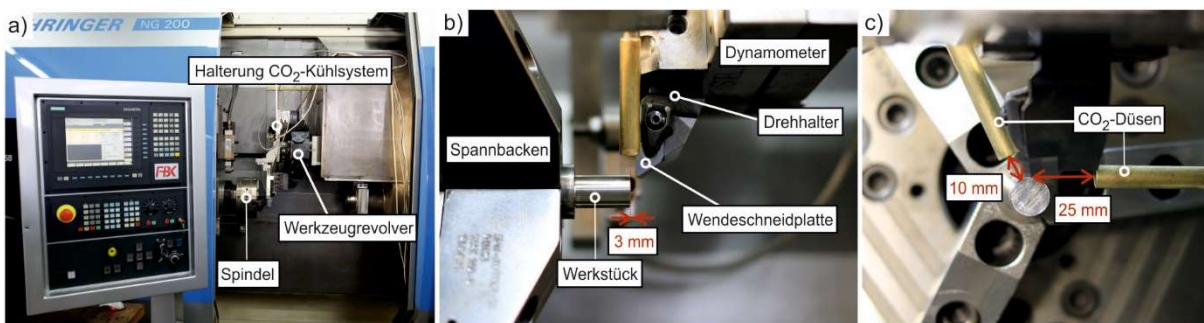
a) Versuchsmaschine Boehringer NG 200; b) Arbeitsraum parallel zur Werkzeugbezugsebene; c) Arbeitsraum parallel zur Werkzeugrückebene; nach [Hotz20a]
